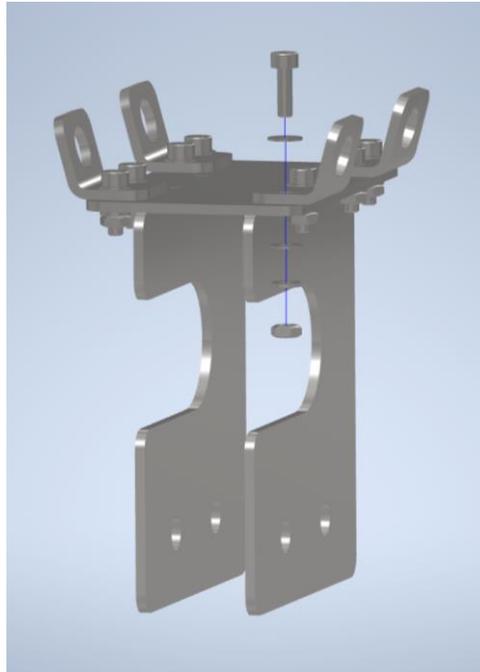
Suporte final montado com realce nos componentes de montagem mecânica
